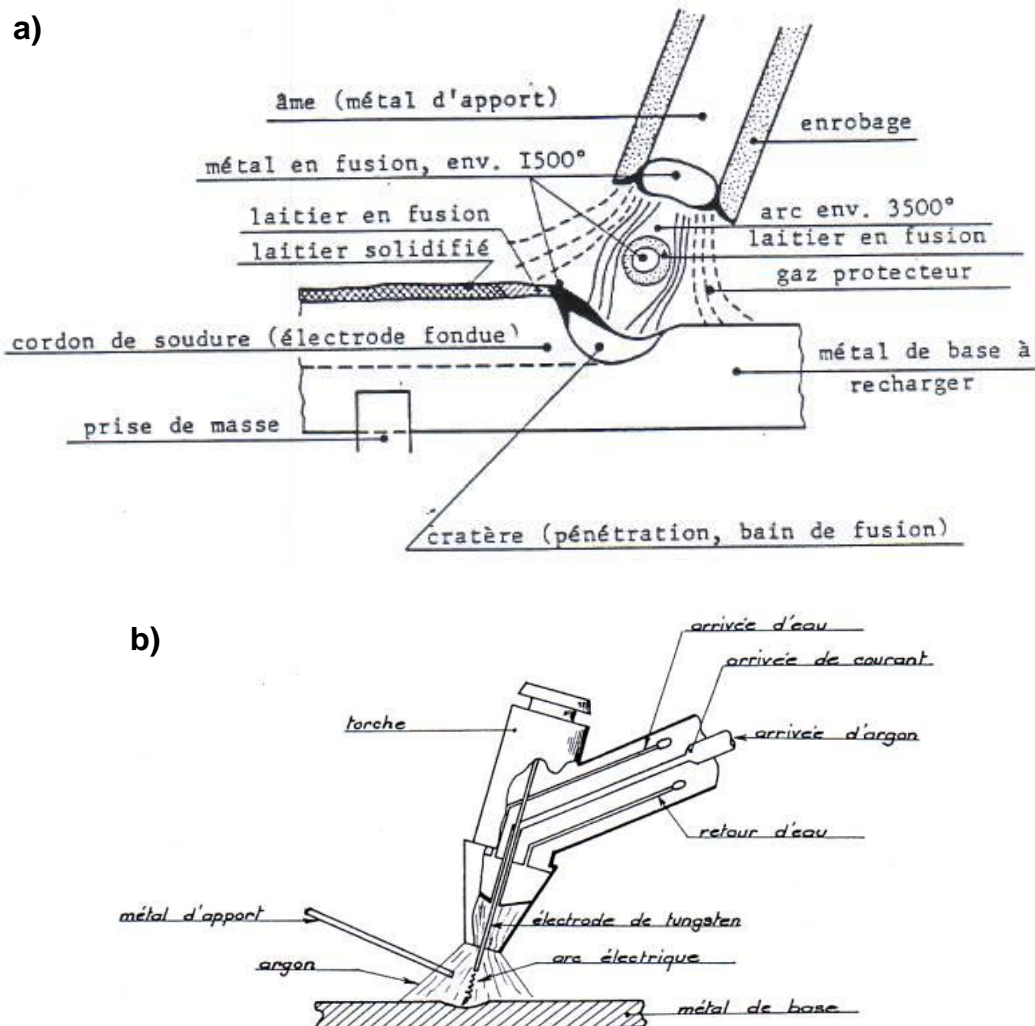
Schémas de principe des techniques de soudage à l'arc (a) à l'électrode enrobée et (b) Tungsten Inert Gas [92]
